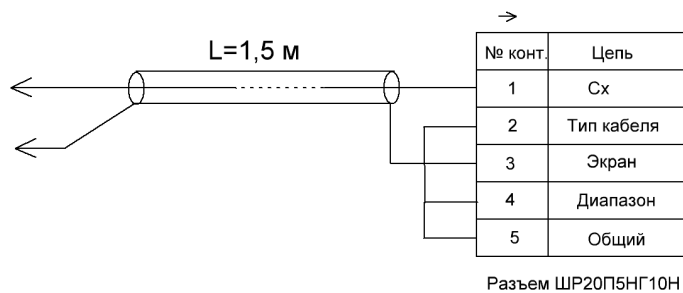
а. Схема монтажная кабеля соединительного КС-1.
